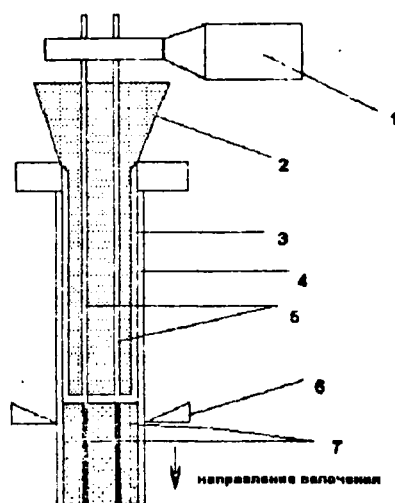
Схема засыпки порошковой изоляцией кабельной заготовки с использованием ультразвуковых колебаний: 1-магнитострикционный преобразователь-концентратор, 2-бункер, 3-направляющая труба (шток), 4-труба-заготовка, 5-направляющие трубки для жил, 6- вибратор, 7- гокопроводящие жилы.
